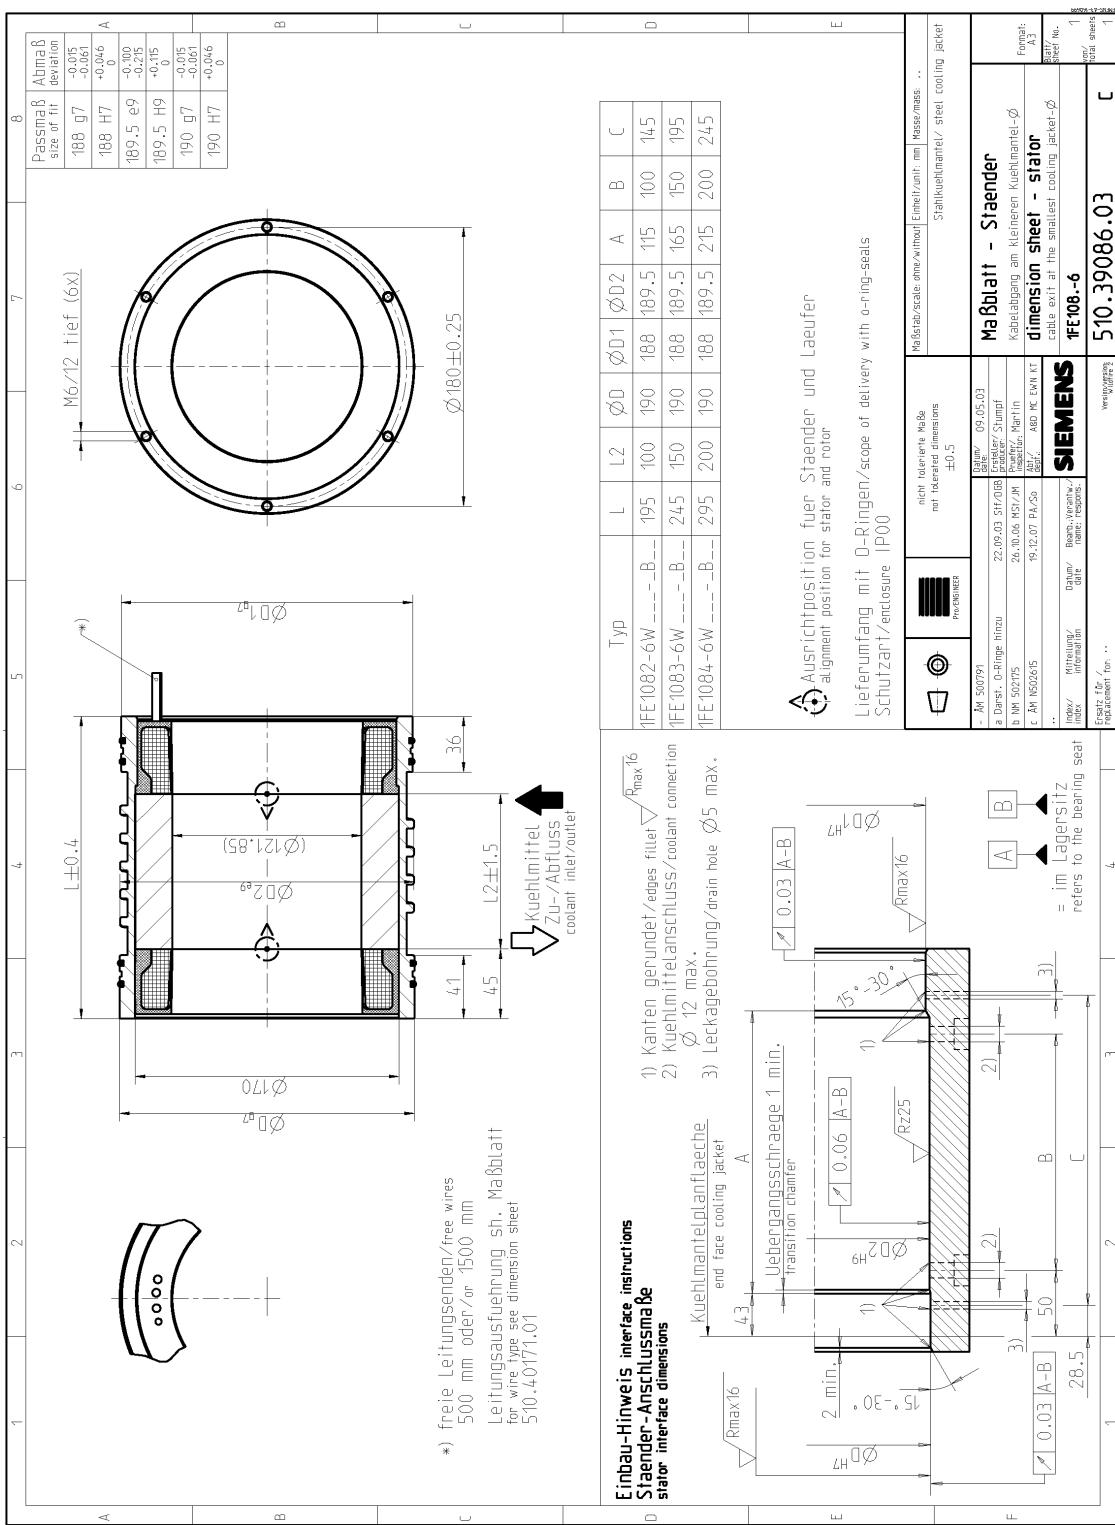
1FE108□-6, Ständer mit Kühlmantel, Kabelabgang am kleineren Kühlmanteldurchmesser
